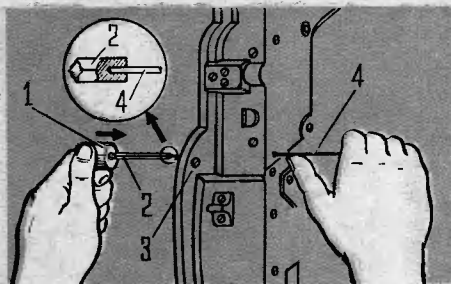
Постановка наружного выключателя замка двери у «Волги» и «Победы»: 1 — выключатель; 2 — стержень; 3 — винт крепления выключателя; 4 — проволока.
